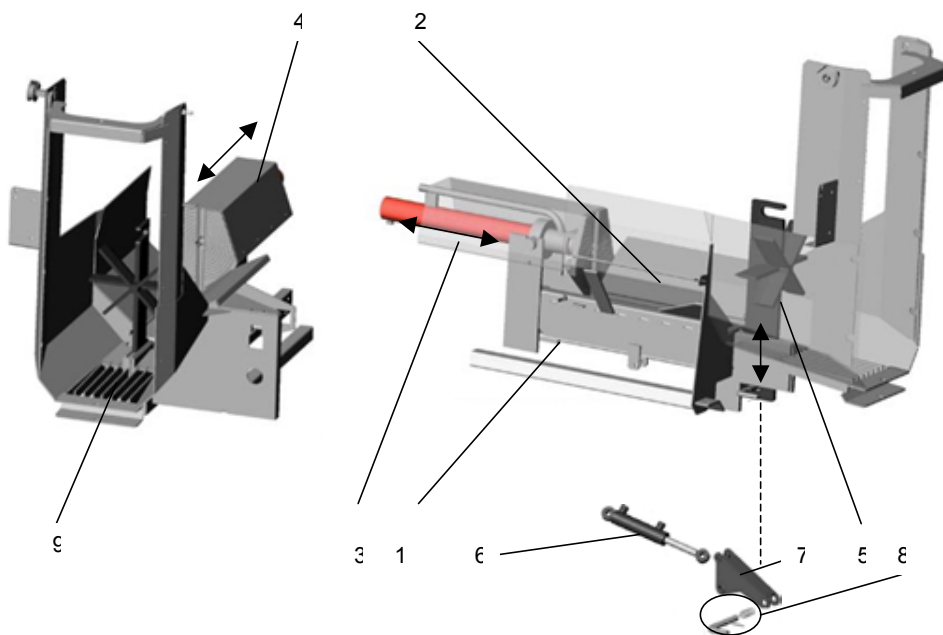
Гидравлический раскалывающий механизм Palax Power 100S: 1 – рама; 2 – лоток; 3 – силовой гидроцилиндр; 4 – толкатель; 5 – нож; 6 – гидроцилиндр; 7 – подъемная тяга; 8 – пружина, стопорный штифт, клин; 9 – решетка
